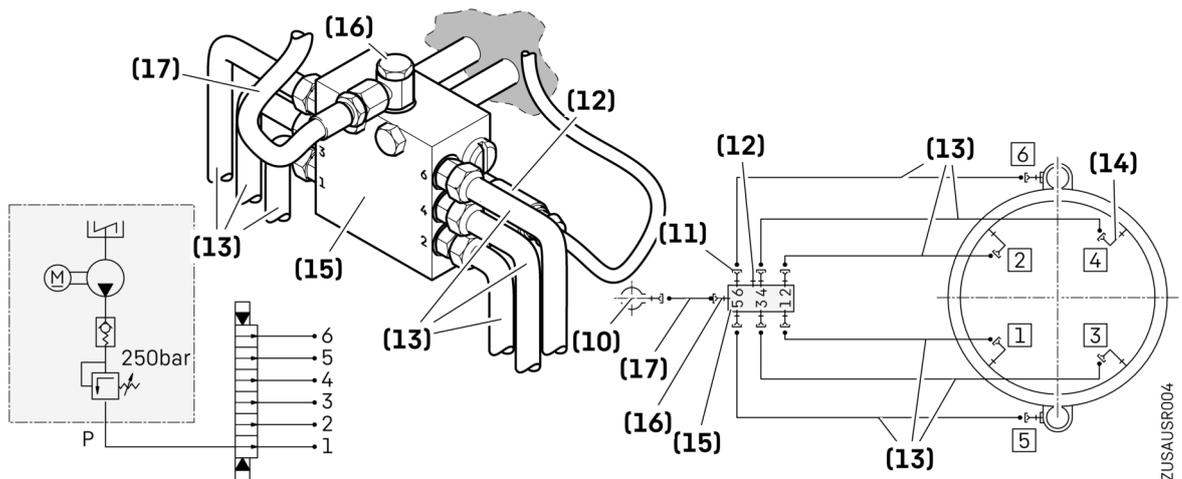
Verlegeplan und Hydraulik-Schaltplan (6er-Verteiler mit zwei Drehwerken)
